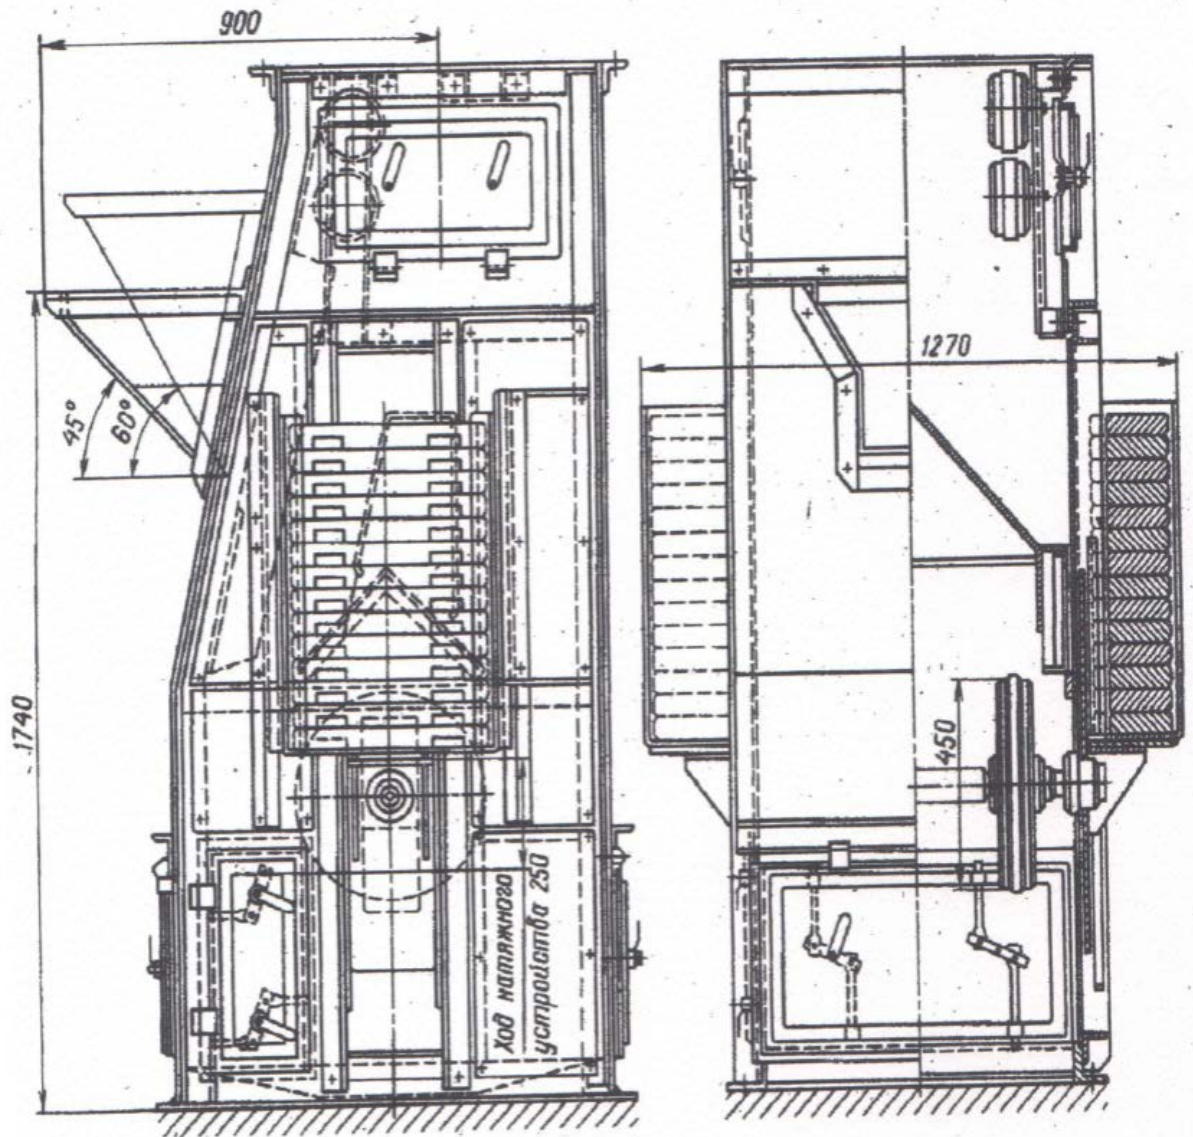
Нижняя часть кожуха и грузовое натяжное устройство вертикального ковшового цепного элеватора
